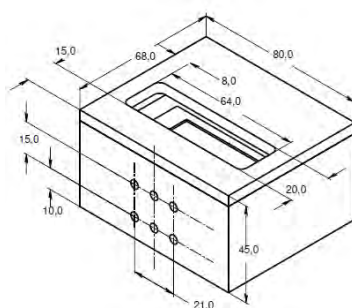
D Dibujo técnico del paquete y los agujeros de montaje del MMDM
